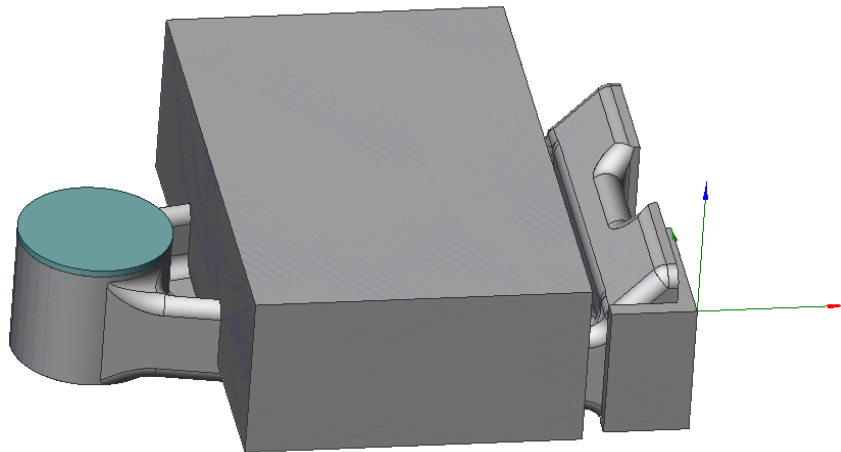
Базування та нульова точка координат заготовки при Базуванні 3
